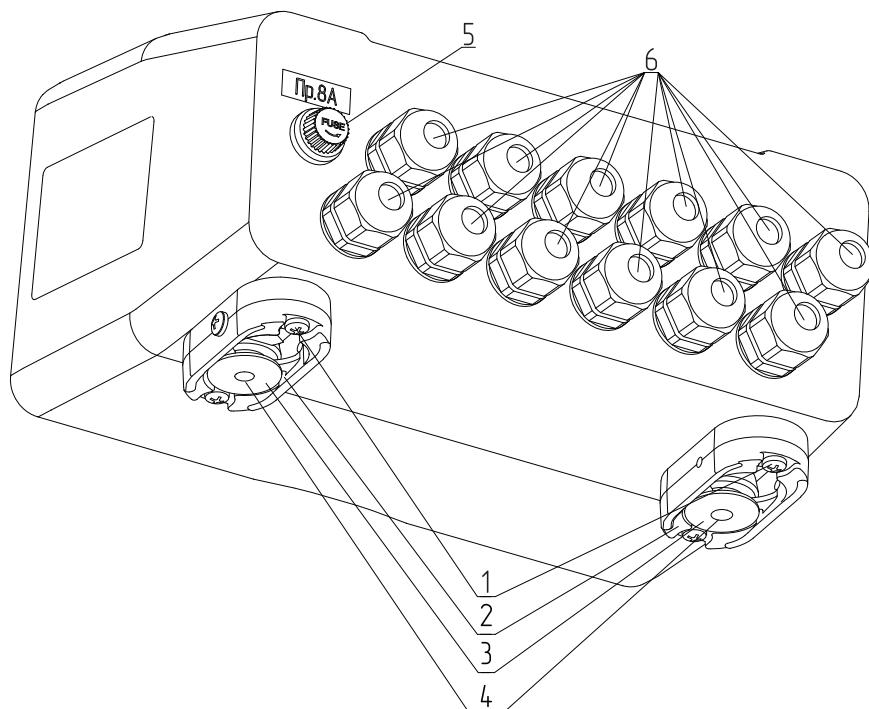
Внешний вид контроллера C-Line 200PA с фиксатором крепления
